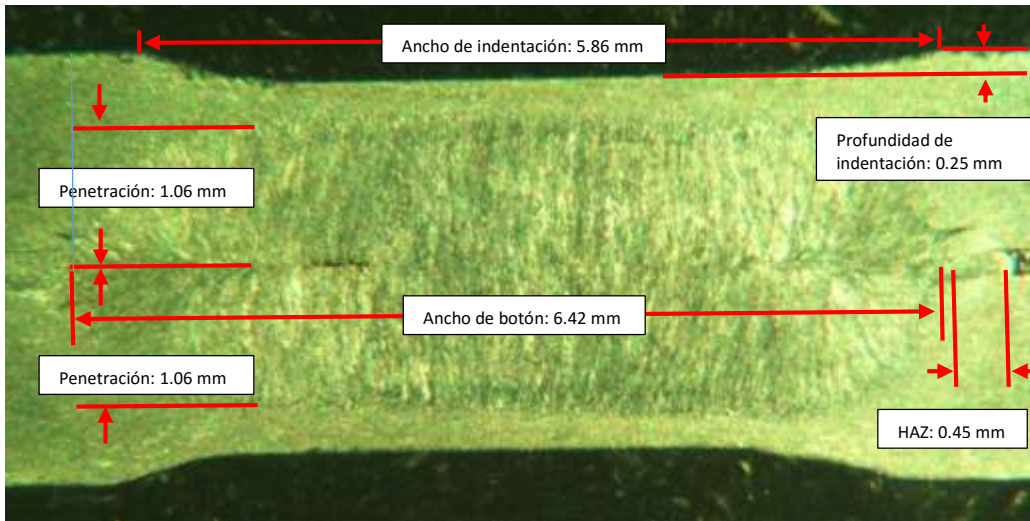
Mediciones realizadas en el botón de soldadura número 19.
